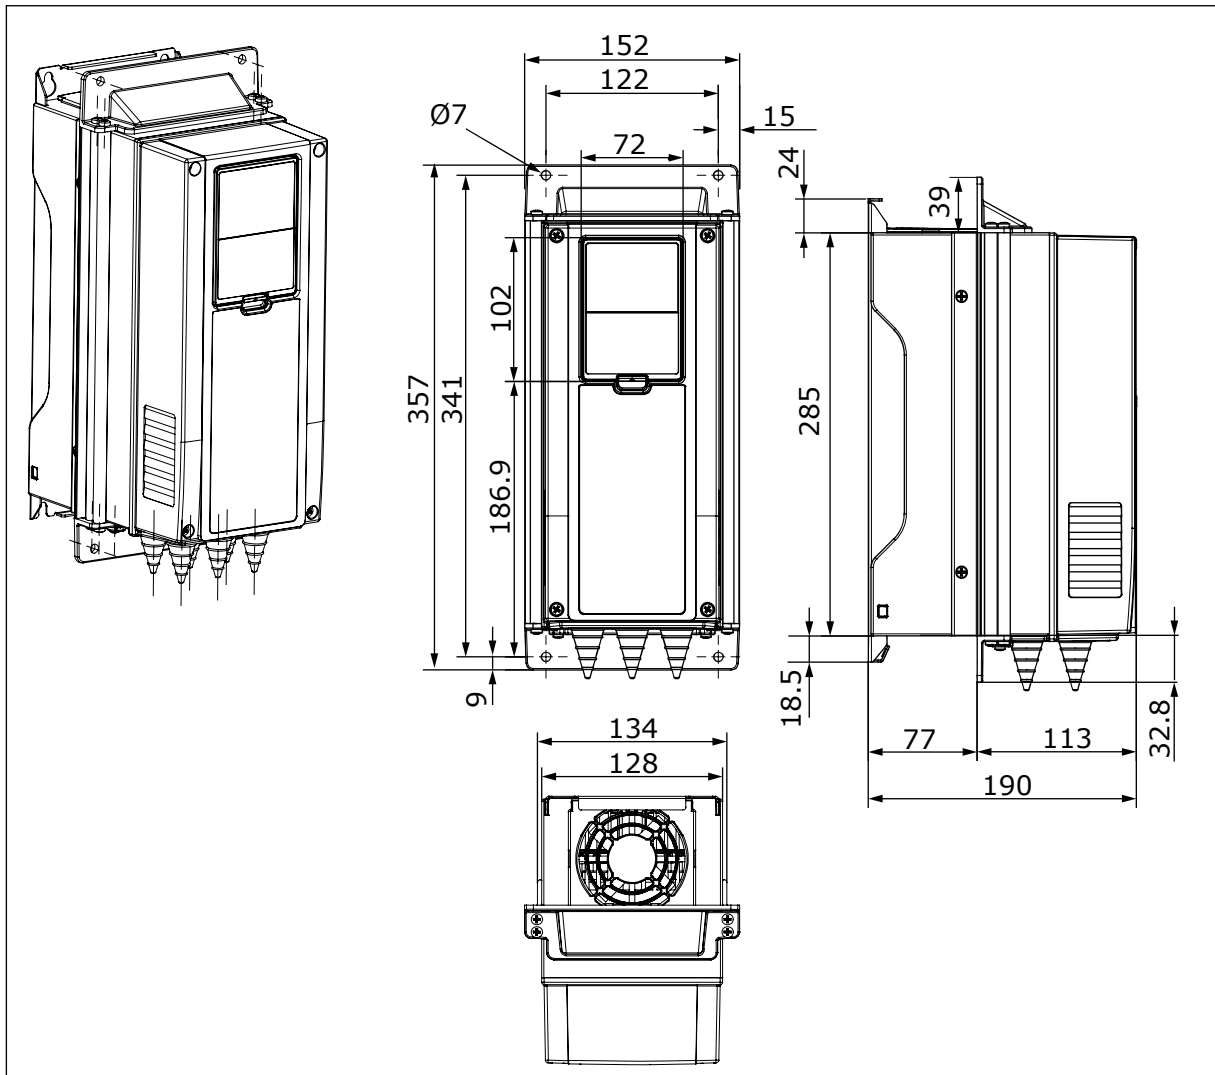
Dimensioni dell'inverter, montaggio a flangia, MR4 [mm]
